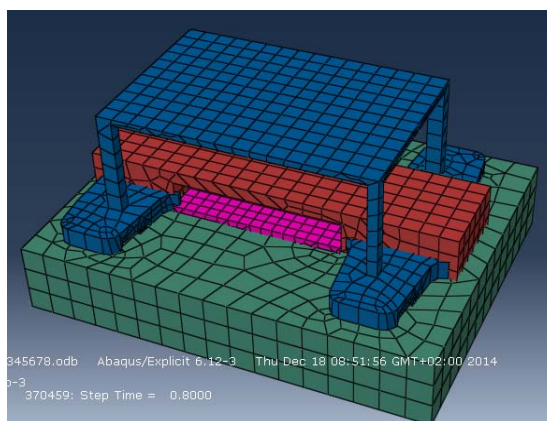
Сборка моделей матрицы штампа, пуансонов и заготовки для расчета НДС металла в САЕ-системе при поэтапной штамповке поковки имплантата
